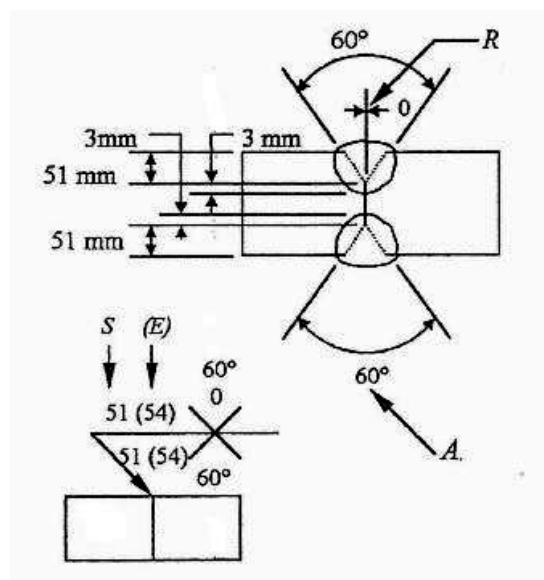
Dimensiones en los símbolos de soldadura de ranura.
